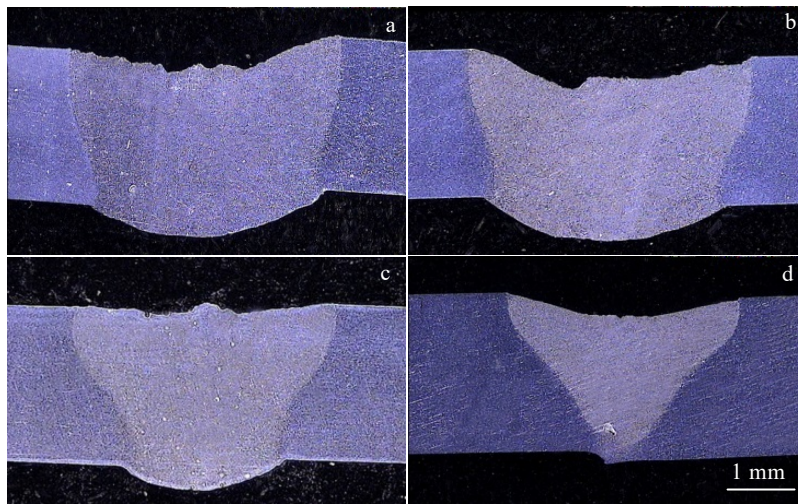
不同焊接速度下 ZrB_{2p}/6061Al 复合材料焊缝宏观形貌
